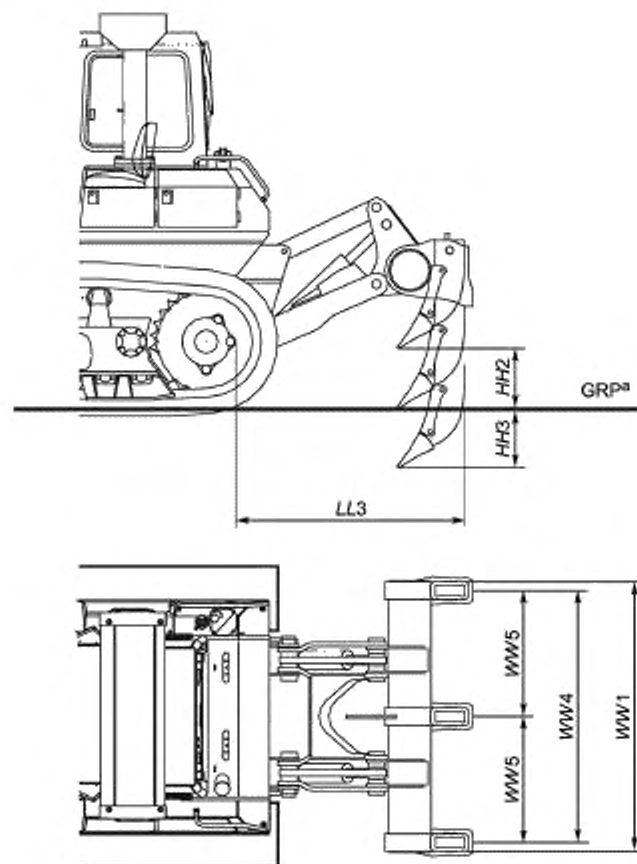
Размеры гусеничного бульдозера с рабочим оборудованием
